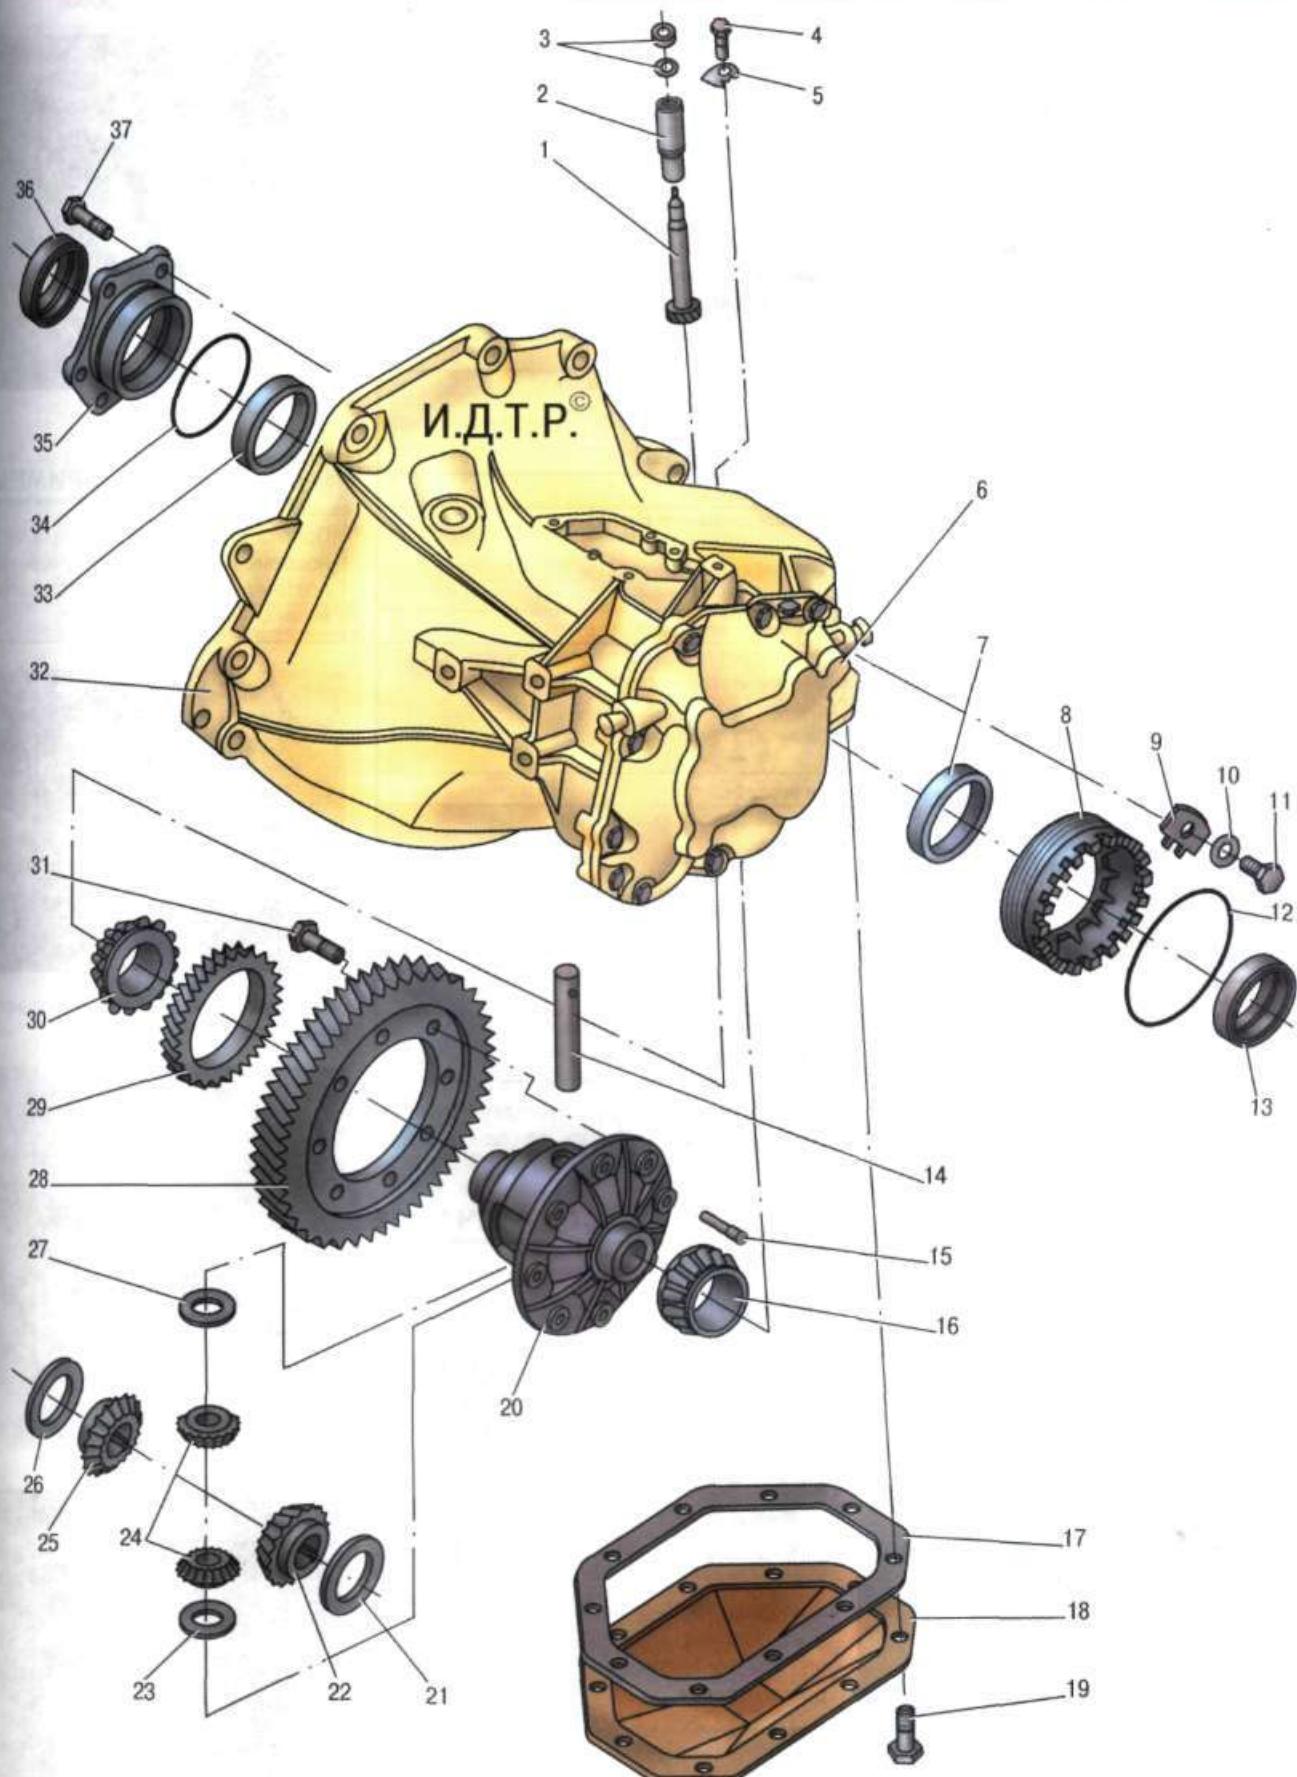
Главная передача и дифференциал: 1 – вал-шестерня редуктора привода спидометра; 2 – корпус редуктора привода спидометра; 3, 12, 34 – уплотнительные кольца; 4, 11, 19, 31, 37 – болты; 5 – стопорная пластина; 6 – крышка коробки передач; 7, 33 – наружные кольца подшипников дифференциала; 8 – регулировочная гайка подшипников; 9 – пластина фиксатора; 10 – шайба; 11, 36 – сальники; 12 – крышка дифференциала; 13 – конические роликовые подшипники дифференциала; 14 – ось сателлитов дифференциала; 15 – фиксатор оси сателлитов; 16, 30 – конические роликовые подшипники дифференциала; 17 – прокладка; 18 – нижняя крышка; 20 – корпус дифференциала; 21, 26 – упорные шайбы; 22, 25 – полусеевые шестерни; 23, 27 – упорные шайбы сателлитов; 24 – сателлиты; 28 – ведомая шестерня главной передачи; 29 – ведущая шестерня привода спидометра; 32 – картер коробки передач; 35 – правая крышка подшипников дифференциала.
